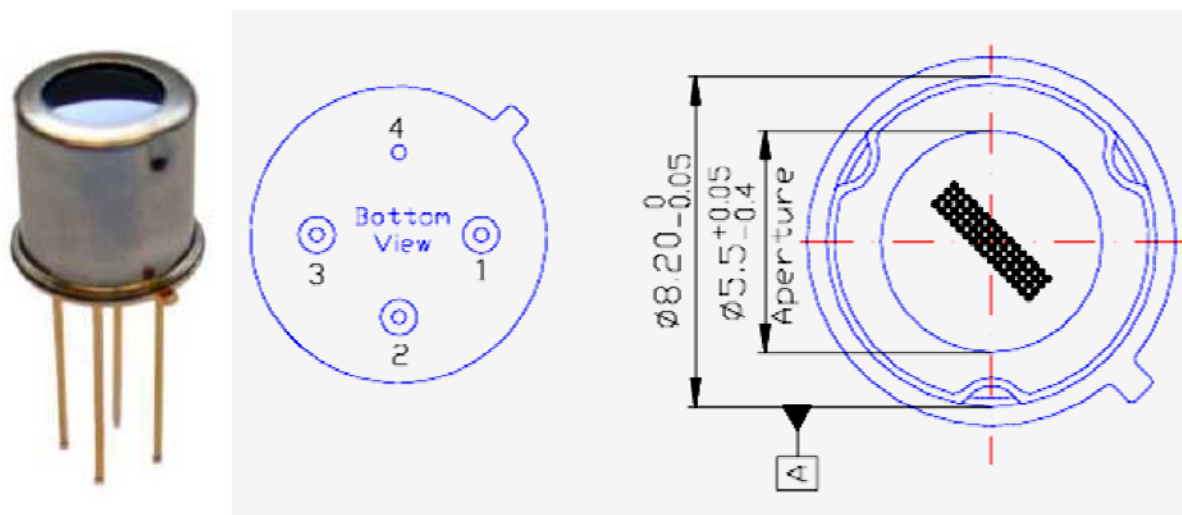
Общий вид сенсоров НТРА16x4 с обозначенными контактами и типовыми размерами
